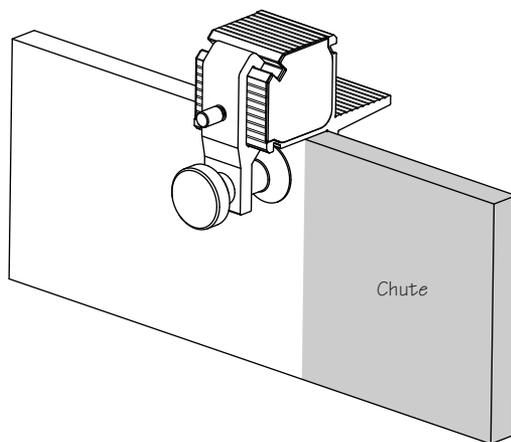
Guide de sciage à angle droit en place et prêt pour la coupe.
